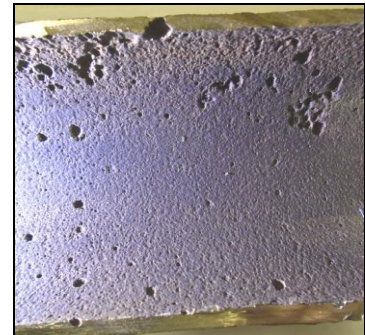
vista interna de tubulação 2 1/2",sch 40. Pite passante
